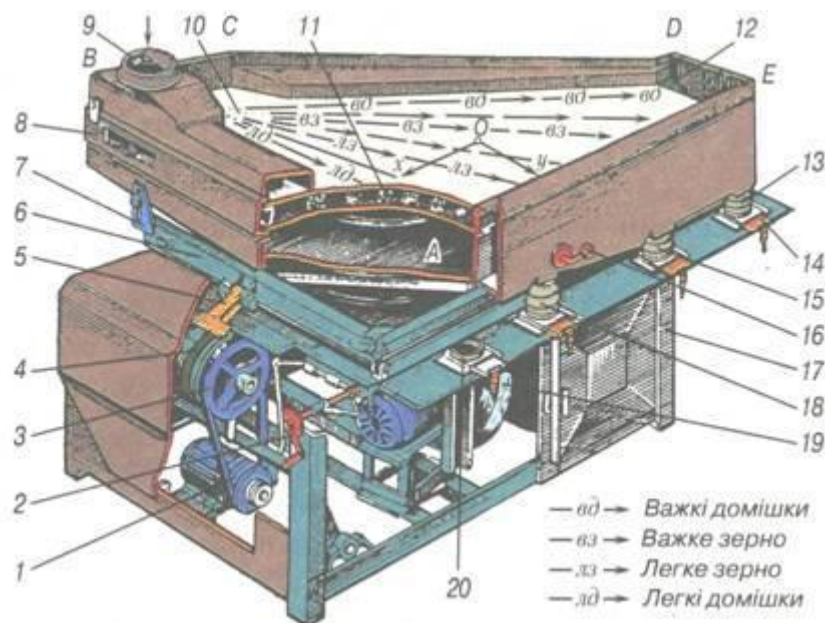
Пневматичний сортувальний стіл ПСС-2.5В:
